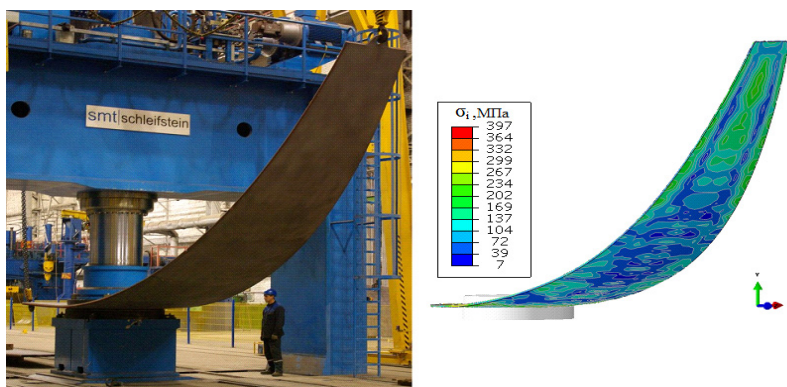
Заготовка шарового резервуара в процессе деформирования
